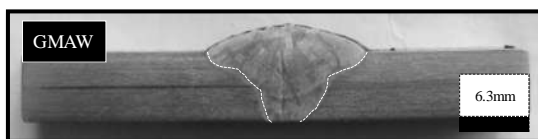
Perfil macroestructural de la unión mediante el proceso de soldadura GMAW
